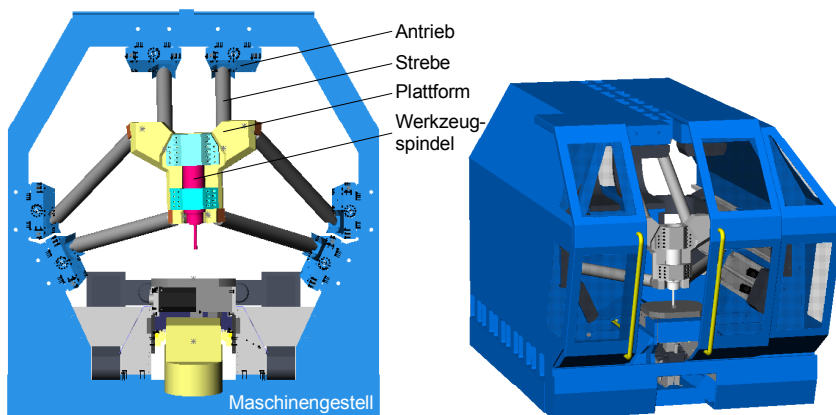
PKM-Werkzeugmaschine PARALIX (Hexapod) in horizontaler Ausrichtung für eine Fünf-Seiten-Bearbeitung.
